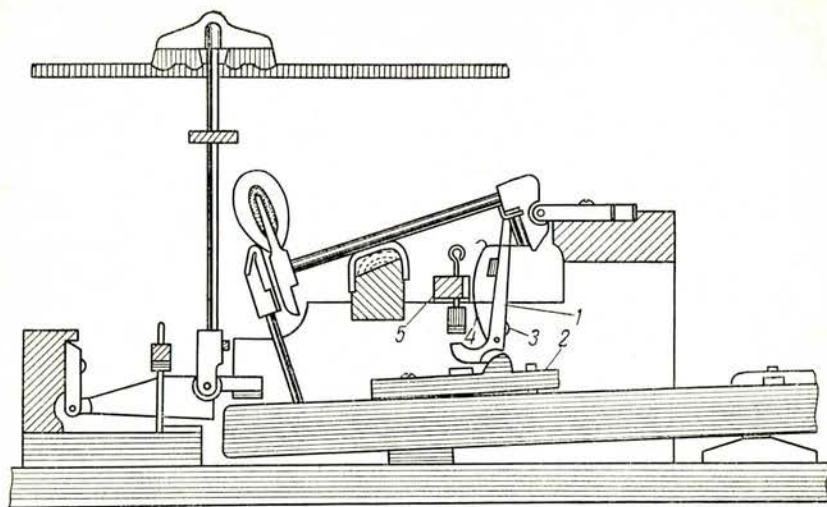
Механизм английской конструкции с добавочной репетицией: 1 — шпилер; 2 — накладной шпилерный винт; 3 — регулировочный винт репетиции; 4 — репетиционная пружина; 5 — ауслезерный узел
